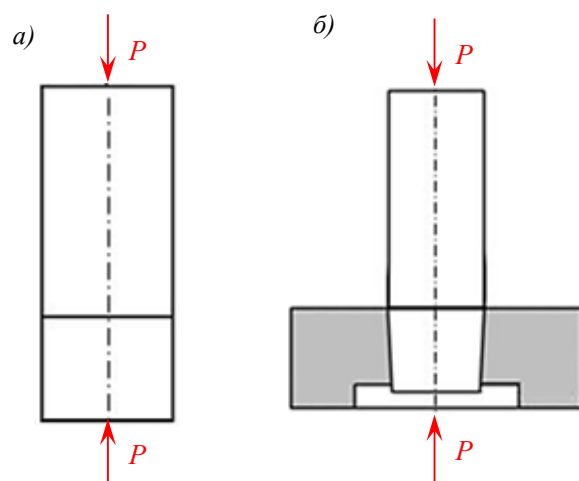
Схема сварки давлением цилиндрических (а) и модельных образцов по схеме «диск–вал» (б) [15]
